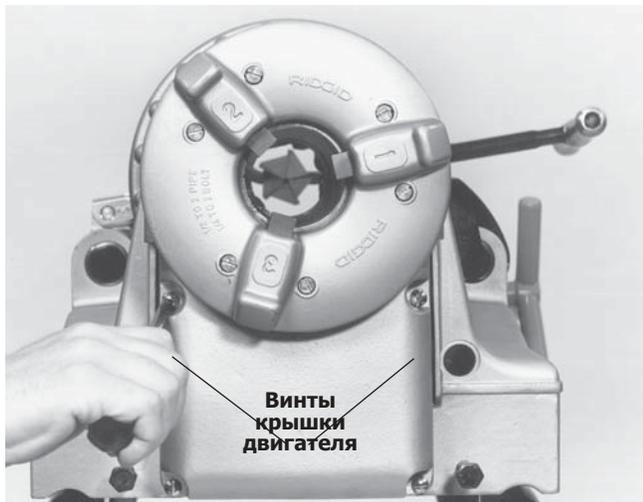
Ослабьте и вытащите винты крышки двигателя
